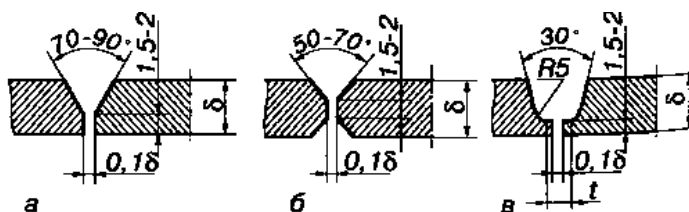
Разделки кромок для многослойной сварки стыковых соединений из титана разных толщин: а – $\delta=4-10$ мм; б – $\delta=10-25$ мм; в – $\delta>25$ мм
